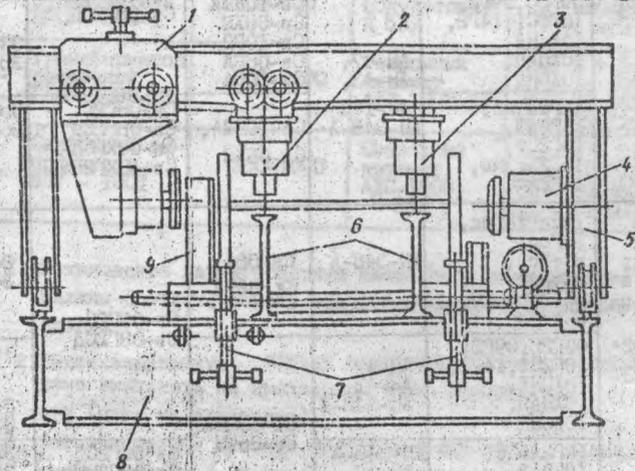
Установка с передвижным порталом для сборки балок: 1, 2-передвижные пневматические прижимы; 3, 4-неподвижные пневматические прижимы; 5-передвижной портал; 6-продольные балки; 7-вертикальные регулировочные винты; 8-рама; 9-стойка-фиксатор.
